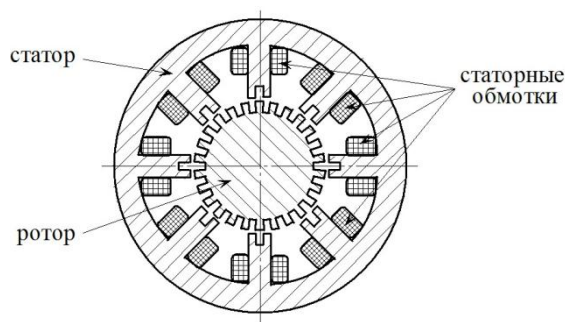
Конструкция ШД с пассивным зубчатым (многополюсным) ротором
